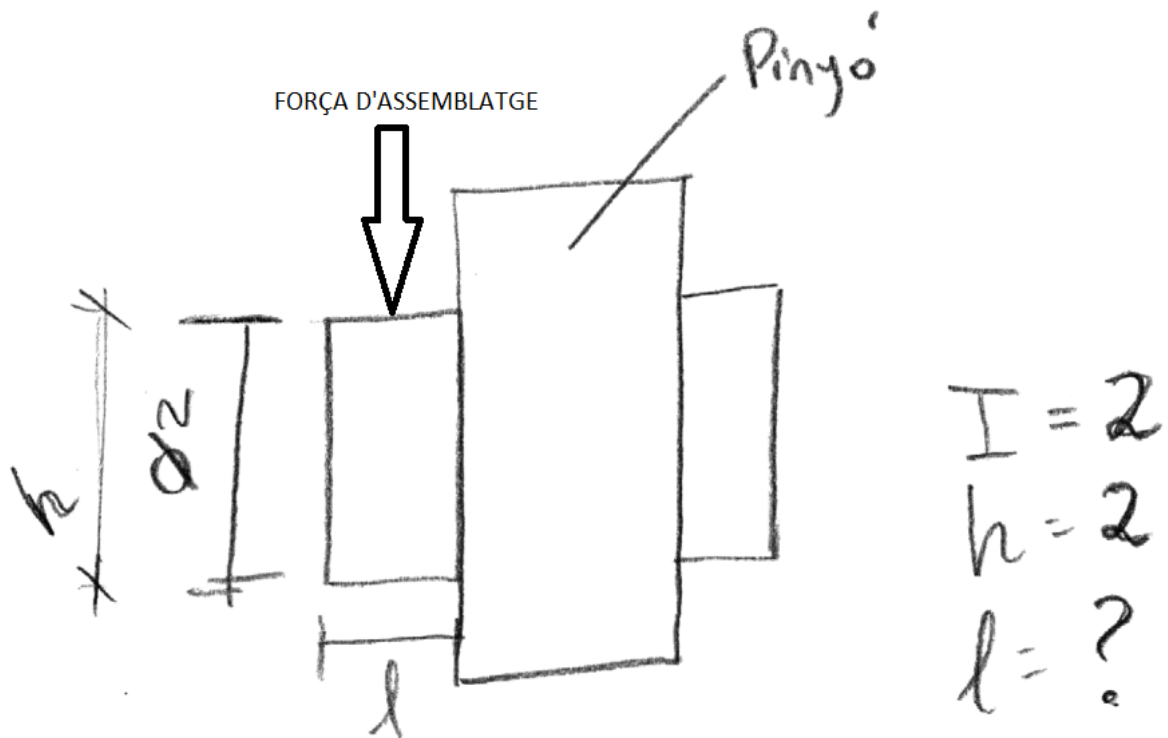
Dimensions de l'element d'unió amb esforç d'assemblatge.
